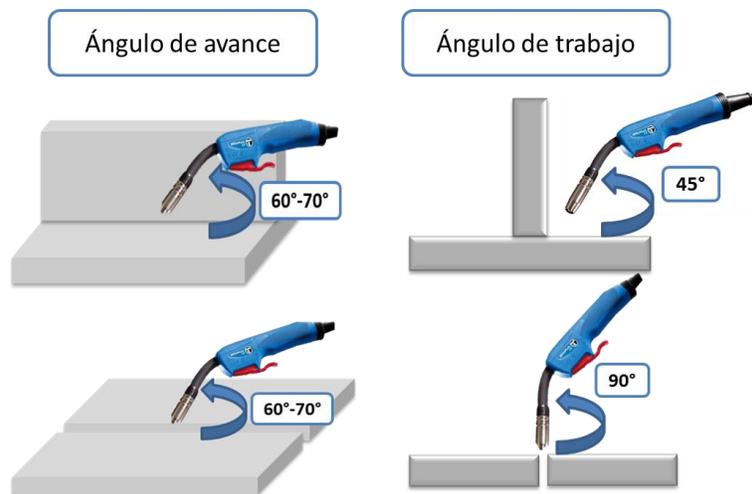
Ángulos de ataque y avance en soldadura GMAW
